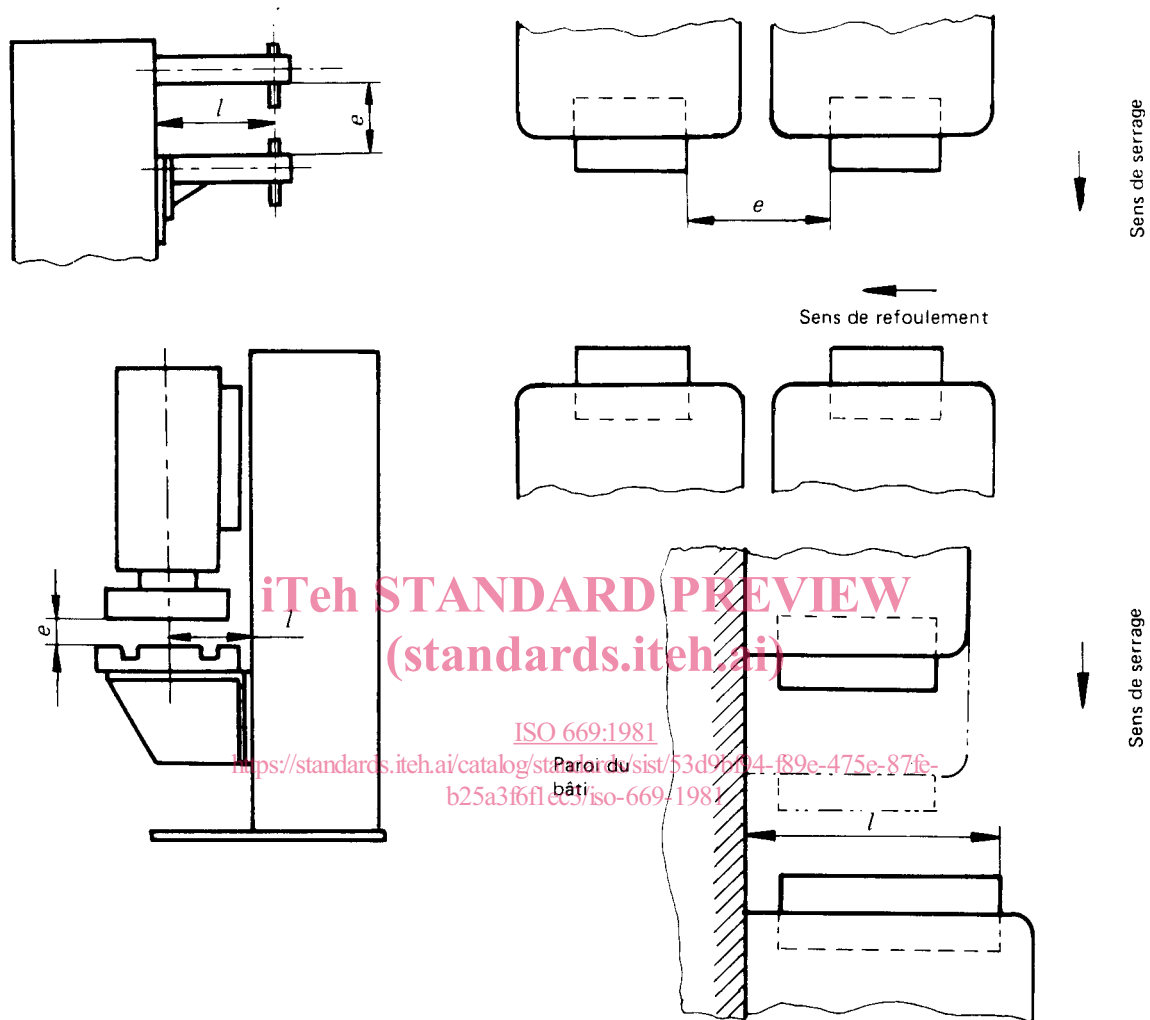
Caractéristiques géométriques d'une machine à souder par résistance
